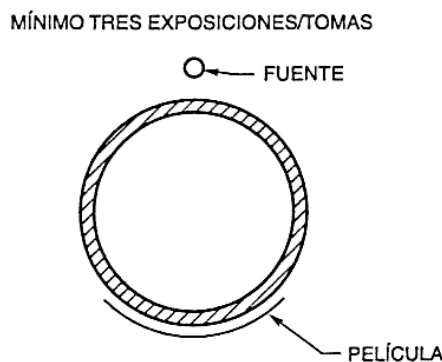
Exposición de una pared-sencilla (vista de la pared sencilla).
